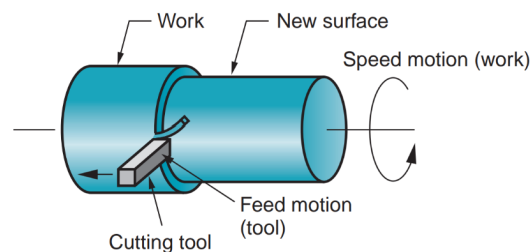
Esquema de maquinagem de objetos pelo processo de tornear [53]
